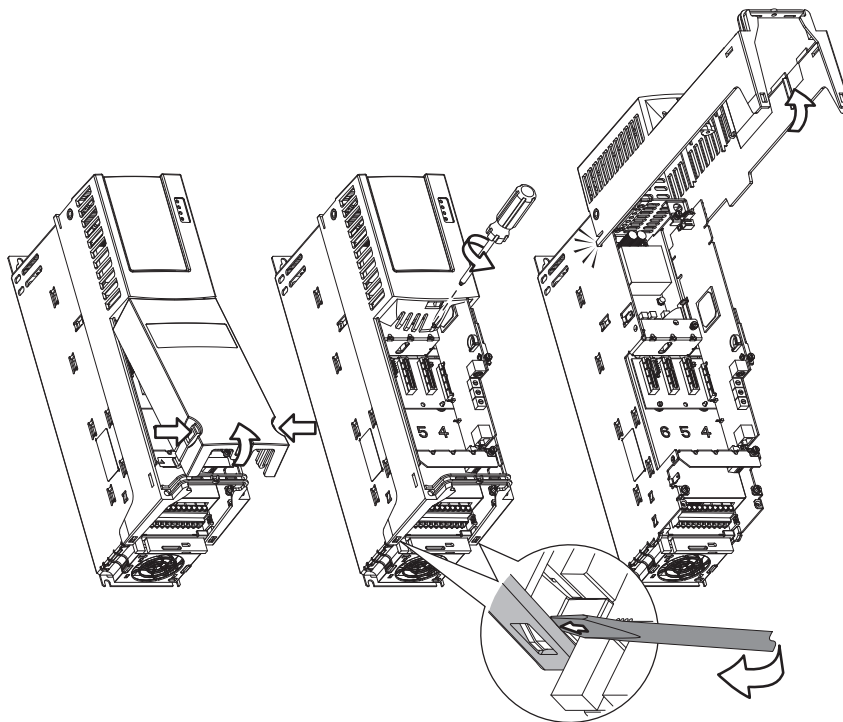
Код корпуса N (IP20, NEMA/UL Open Type), типоразмеры 2–5
